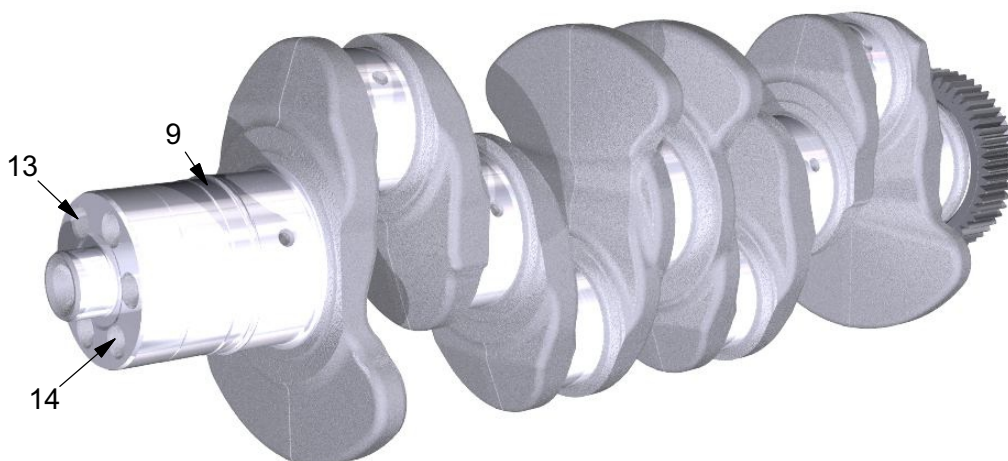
Вал коленчатый (Лист 2 из 3)
